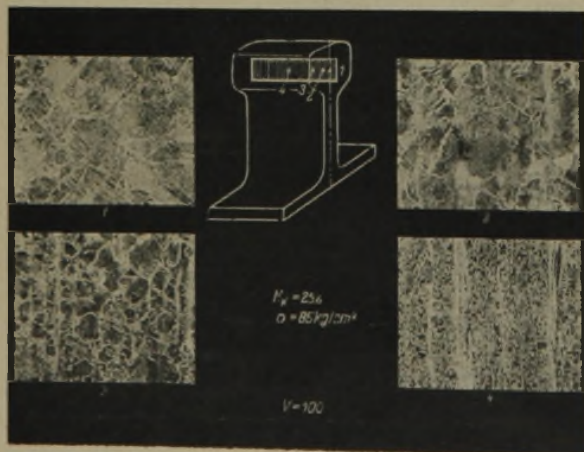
Abbrennschweißung, Gefügebilder geschweißter Eisenbahnschienen
